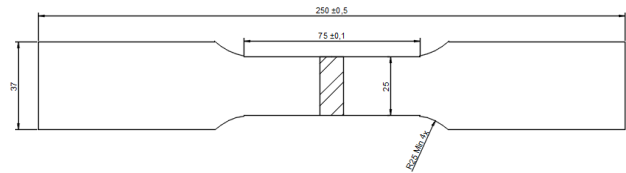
Dimensões do corpo de prova soldados para o ensaio de tração.
